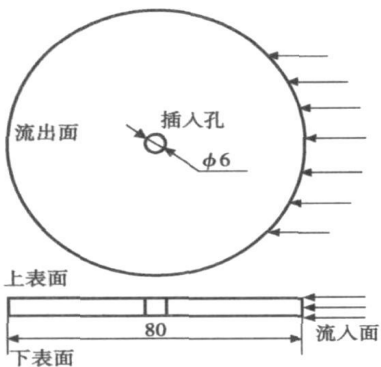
焊接构件尺寸及边界条件(mm)
